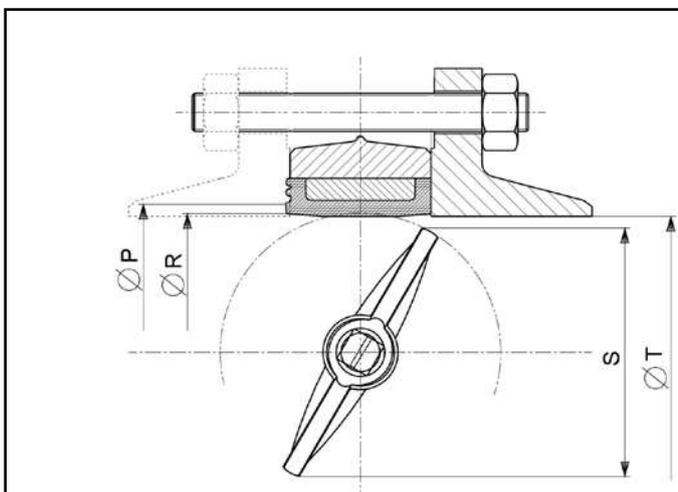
Монтаж дроссельной заслонки в трубопроводе
